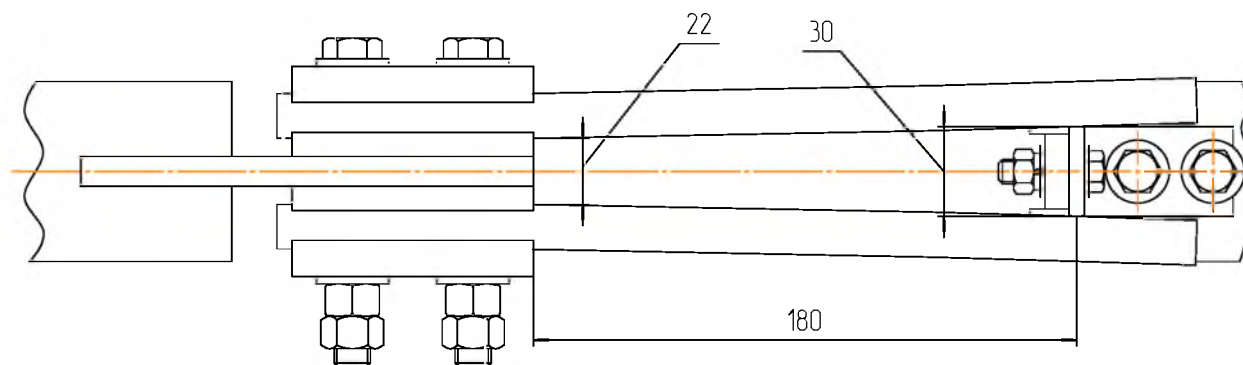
Нож заземления для РГП СЭЩ® -110/1250
